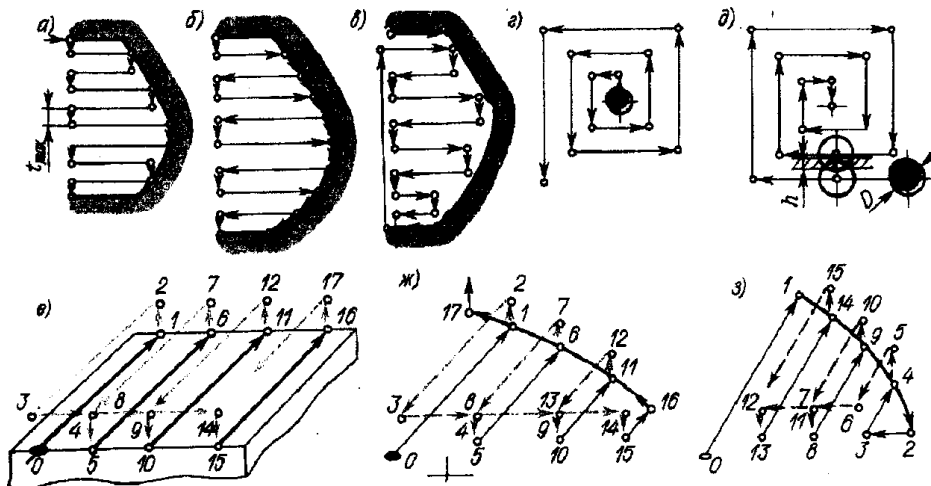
Типовые схемы фрезерных переходов: а – в - зигзагообразные; г, д - спиралевидные; е–з - Ш-образного типа
